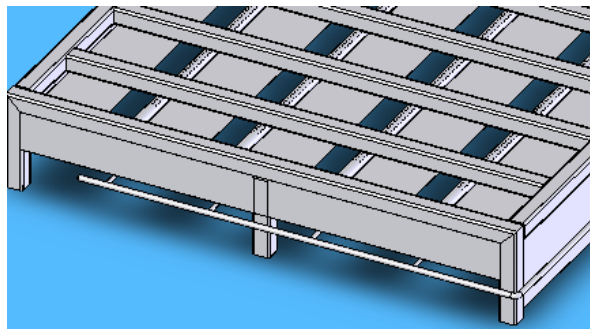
Quemadores de línea instalados en la estructura baja
